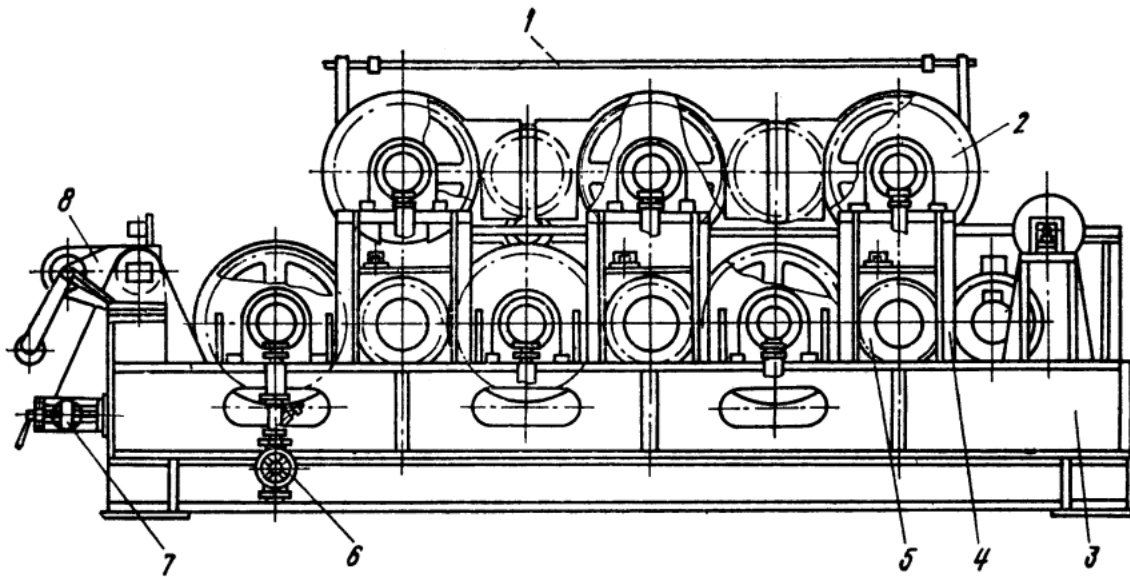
Схема охолоджувального пристрою барабанного типу: 1 – аварійний вимикач тросового типу; 2 – барабан; 3 – рама; 4 – стійки; 5 – зубчаста передача; 6 – вентиль; 7 – натяжний пристрій; 8 – сельсинний датчик
